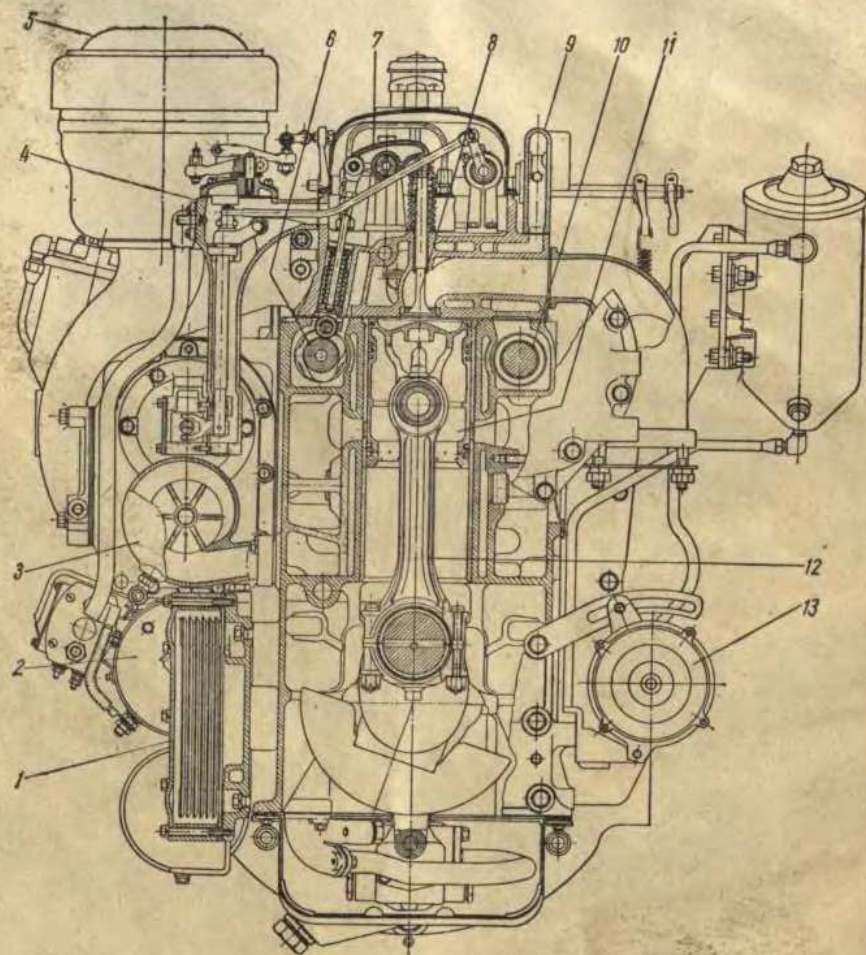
Поперечный разрез двигателя ЯАЗ-М204А.
